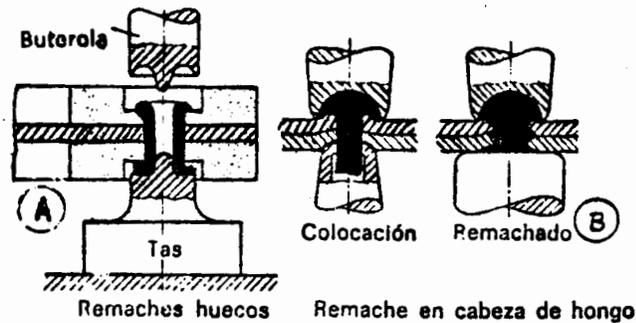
FORMAS ESPECIALES DE REMACHES.
